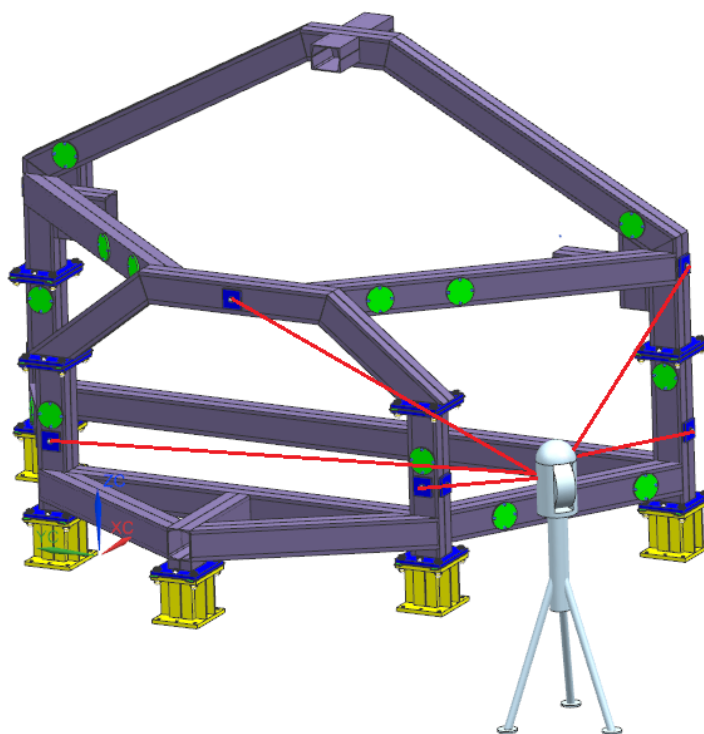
Проверка каркаса сборочного приспособления лазерным трекером.
